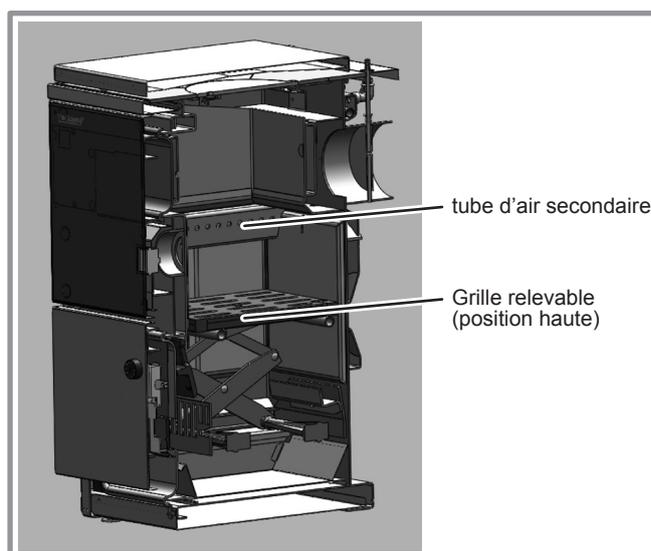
Grille relevable (position haute) : espace de remplissage réduit
